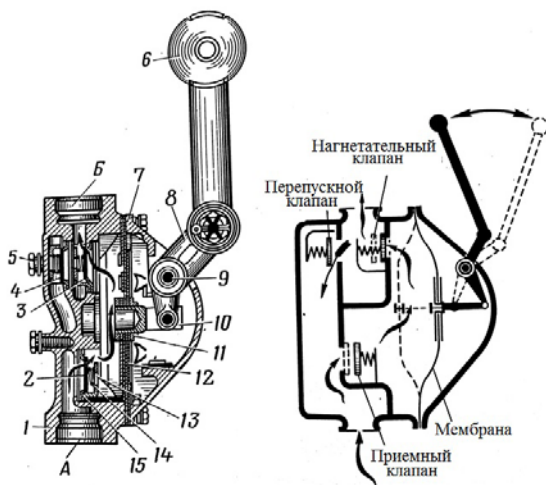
Ручной топливоподкачивающий насос двигателя Д12А-525А:
